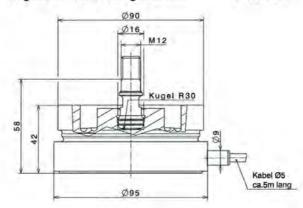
Abmessungen der Wägezelle Typ PR 6261 / Figure 2: Dimensions of the load cell type PR 6261
